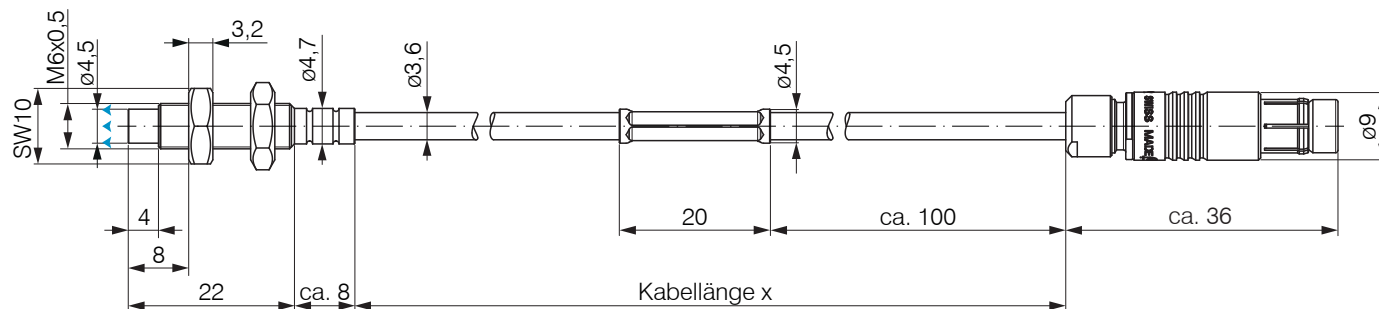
Maßzeichnung Sensoren ES-U1-C-CAx/mB0, Abmessung in mm
